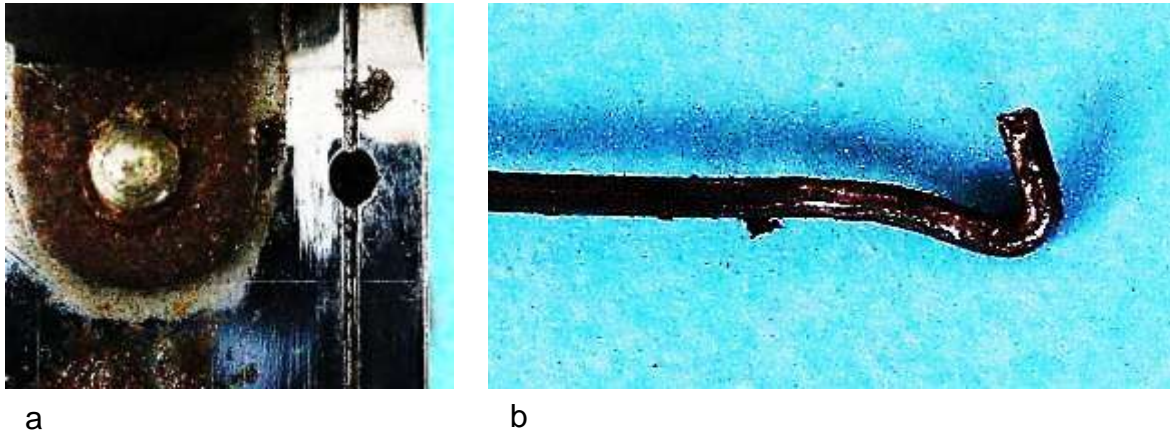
Verschluss: a) Bohrung und Ringnut im Gehäusekopf, b) Haken zum Fixieren des Drahtes in der Bohrung des Gehäusekopfes
